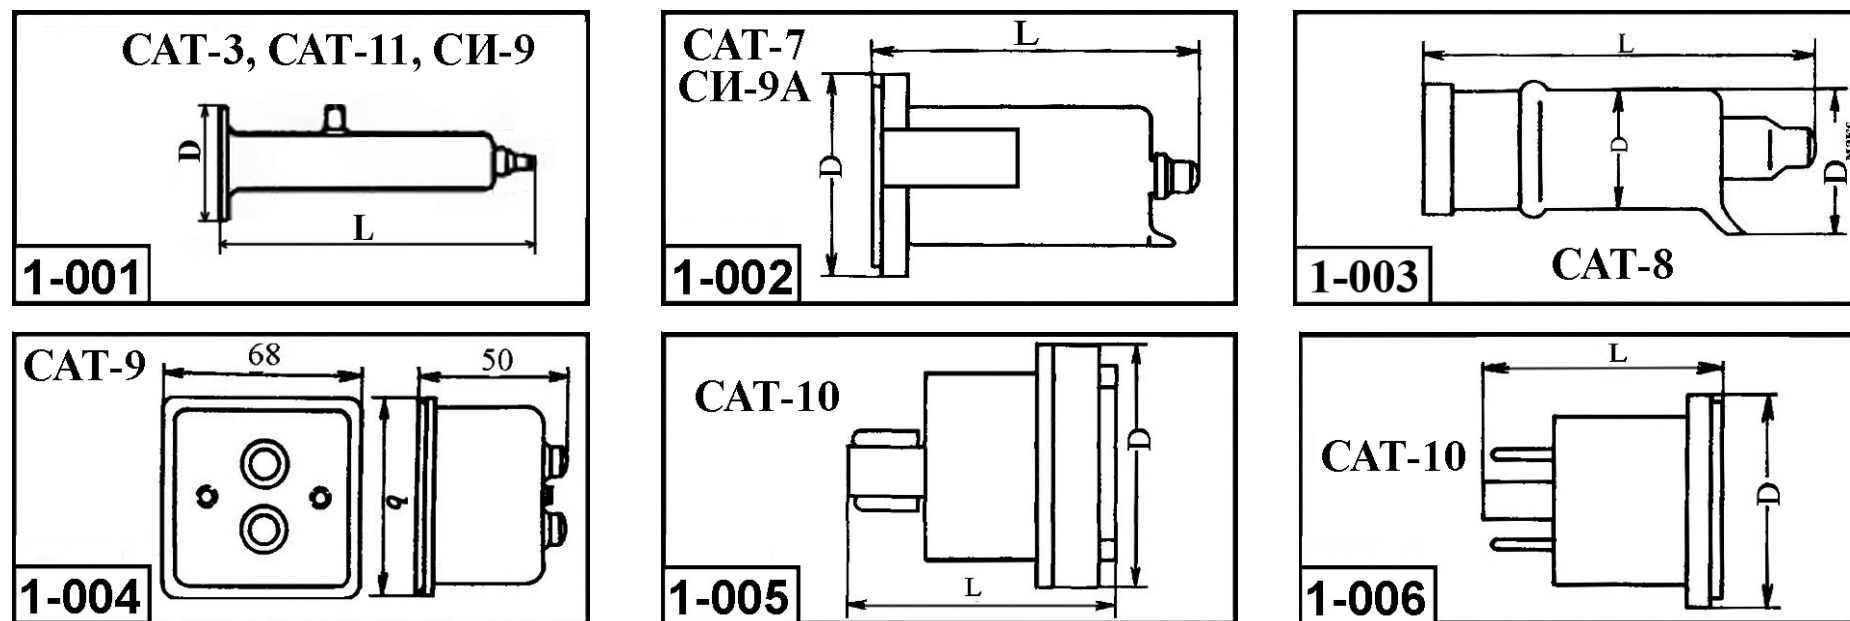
Внешний вид и габаритные размеры детекторов и счетчиков альфа-излучения
